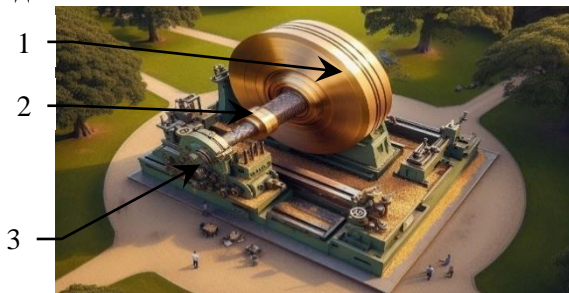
ИИ-интерпретация концепции горизонтально-токарного станка: 1 – обрабатываемая деталь типа диска; 2 – оправка; 3 – шпиндельная бабка
